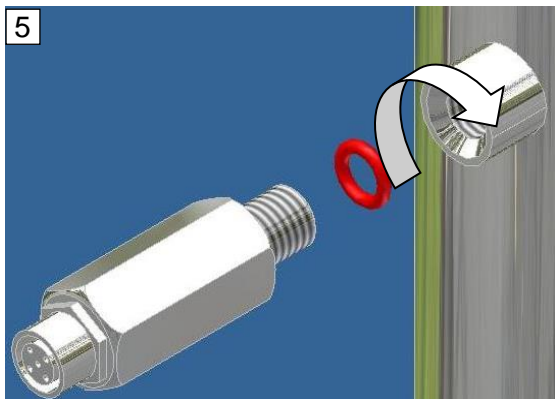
UV-Sensor (JUV 10 - 110 GS)
